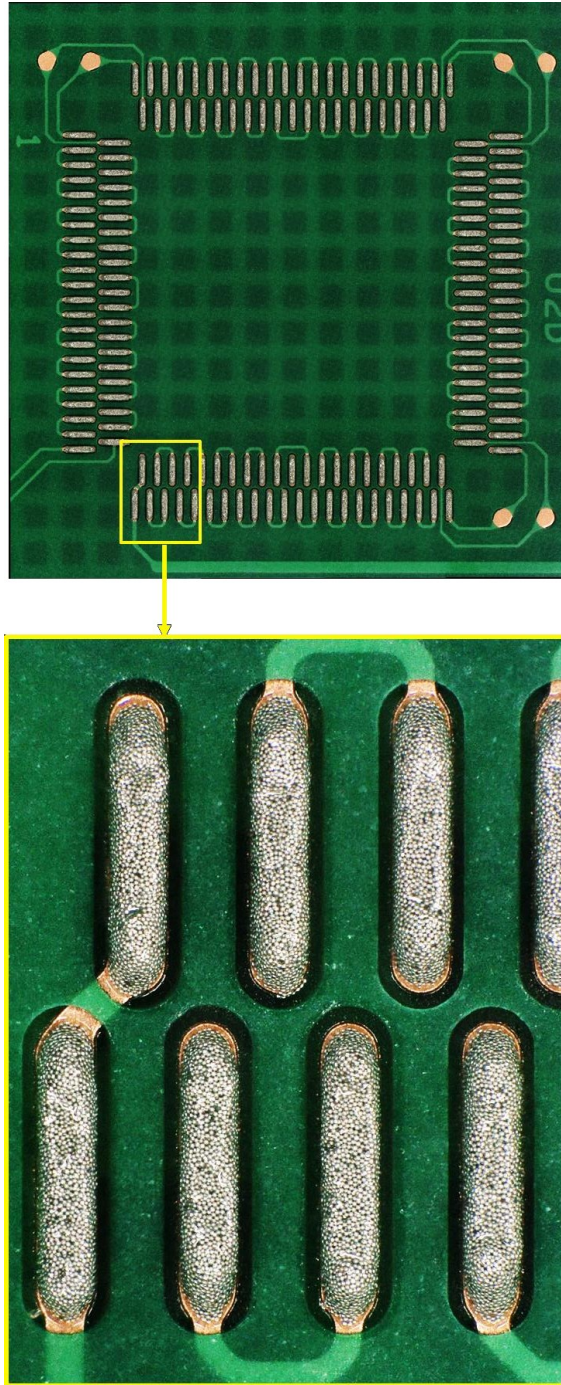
示例：推荐使用焊膏印刷的 172 MaxQFP PCB 脚印
